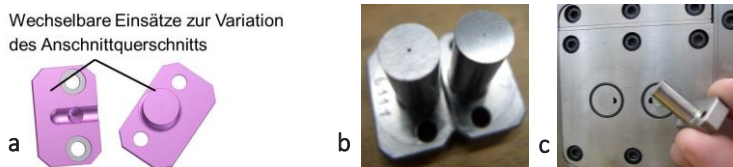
Darstellung der wechselbaren Einsätze zur schnellen Anpassung des Anschnittdurchmessers: a schematisch im 3D-CAD, b Aufnahme zweier Einsätze mit unterschiedlichem Anschnittdurchmesser; c Aufnahme der düsenseitigen Werkzeugplatte, in die die Einsätze eingebaut werden
